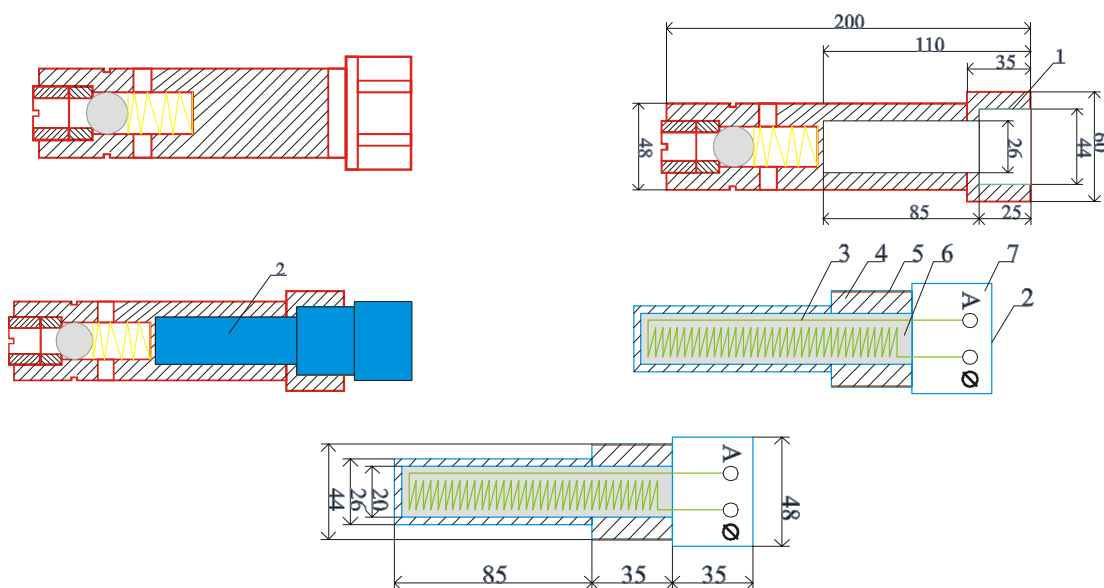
Порядок работы с вёртышем обратного клапана 1 – внутренняя резьба; 2 – термоэлемент; 3 – нагревающее устройство; 4 – корпус термоэлемента; 5 – наружная резьба; 6 – изолирующий материал (в виде порошка); 7 – клемник во взрывозащищённом исполнении ip-54
